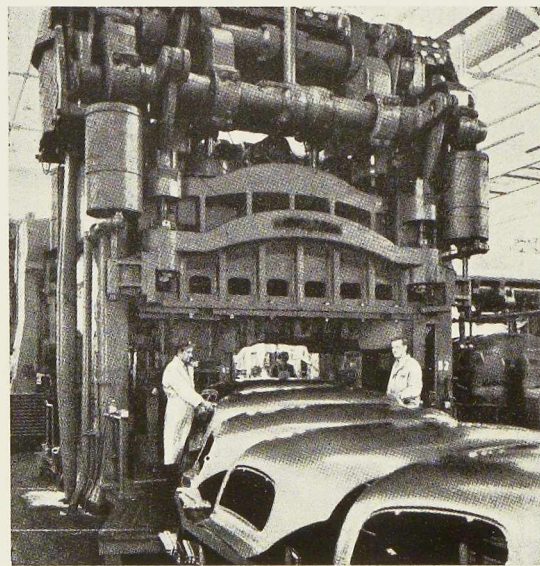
Nouvelle presse géante de la General Motors pour fabrication des carrosseries d'automobiles.
